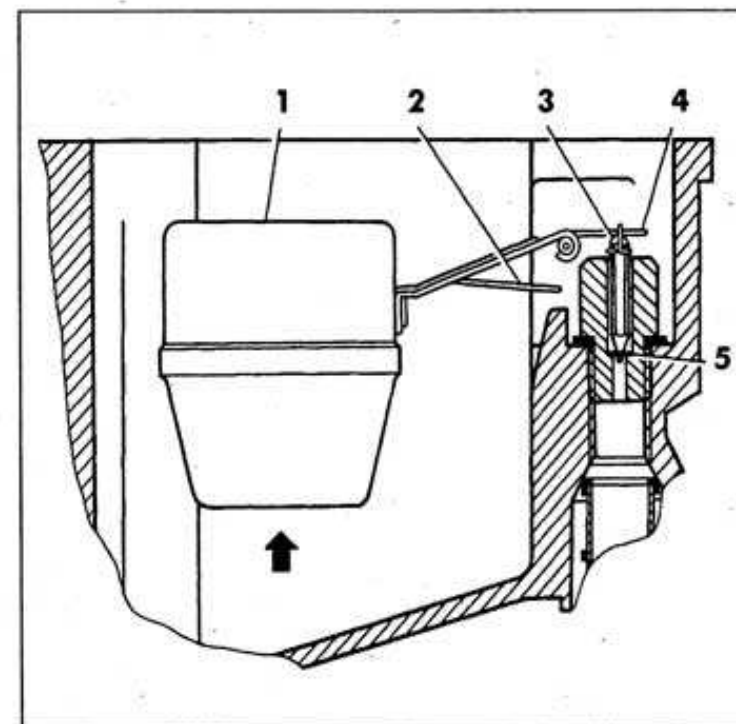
Регулировка поплавого механизма: 1 – поплавок; 2 – язычок для регулировки хода клапана; 3 – клапан; 4 – язычок для регулировки уровня топлива; 5 – уплотнительная шайба
